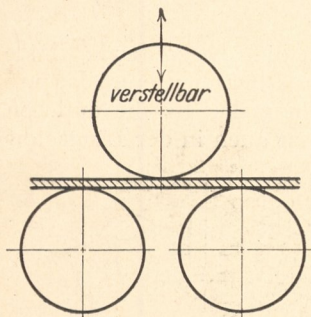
Schema der Dreiwalzen-Biegemaschine.
